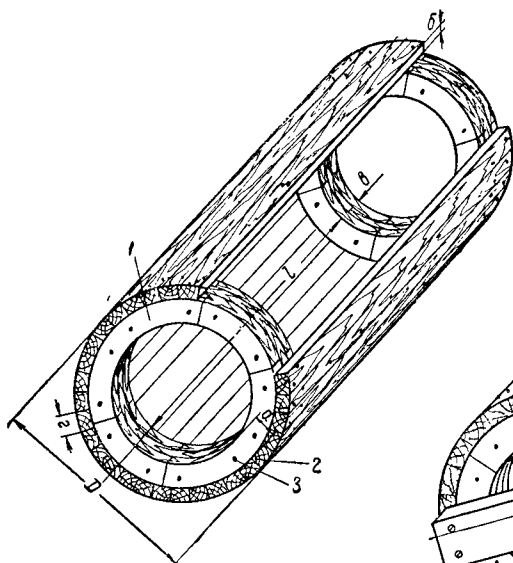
Барабан из клепки на дисках: 1 — диск; 2 — ребро; 3 — клепка (размеры см. в табл. 121).
